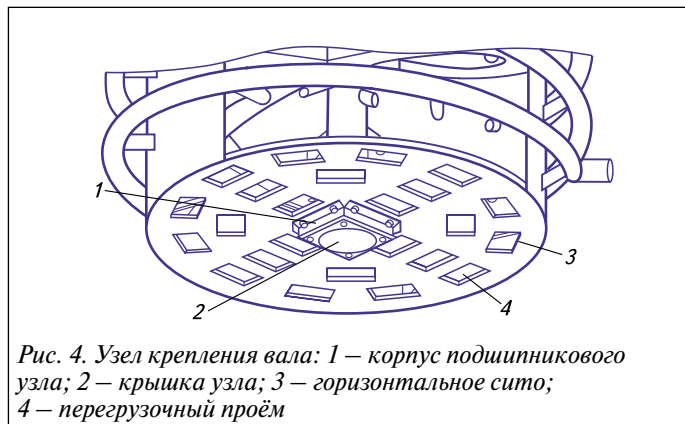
Узел крепления вала: *1* – корпус подшипникового узла; *2* – крышка узла; *3* – горизонтальное сито; *4* – перегрузочный проём
